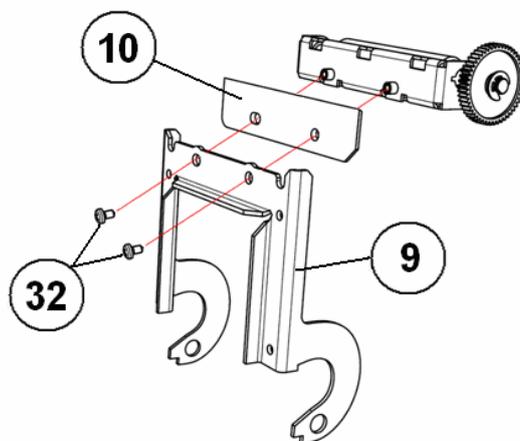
Крепление механизма прижимного вала чековой ленты.
